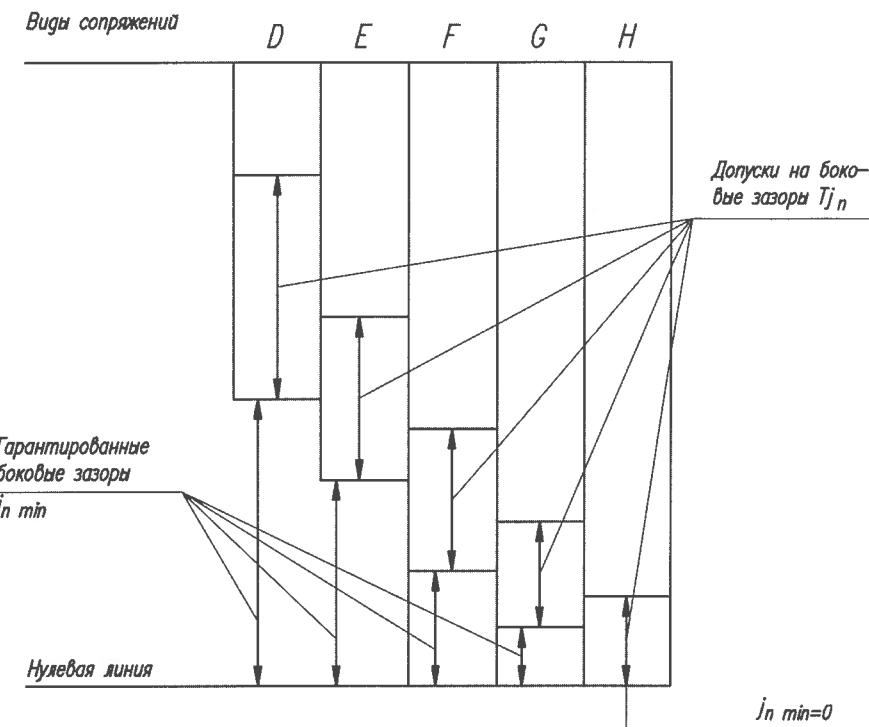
Расположение полей допусков видов сопряжений зубчатых колес
